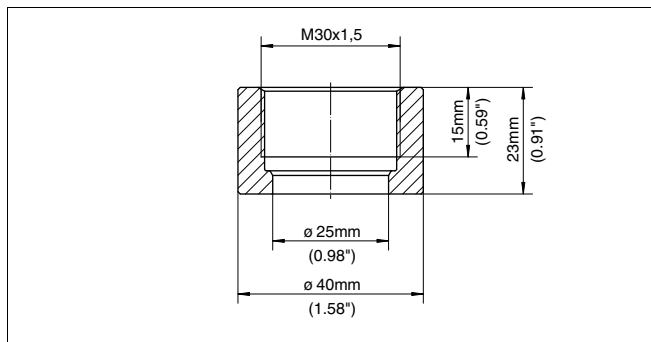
Размеры приварного штуцера M30 x 1,5 для слива бумажной массы
